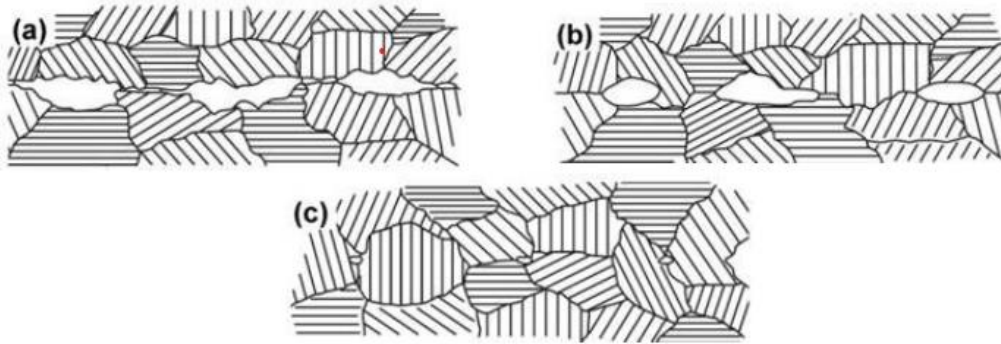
Schéma de principe de soudage par diffusion [12].
